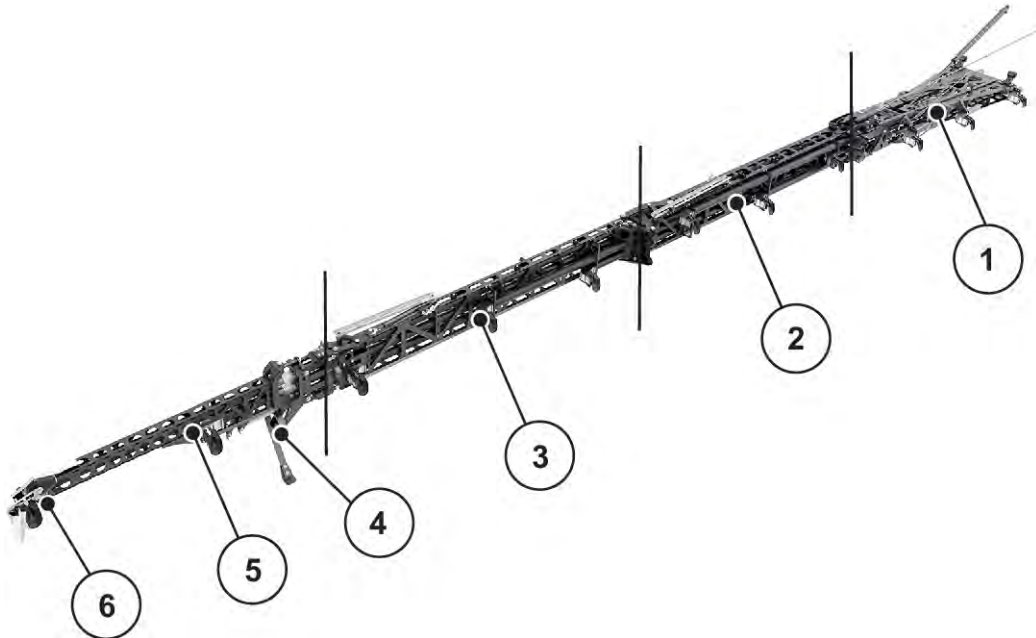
Maskinens komponentgrupper og funksjoner, utligger
